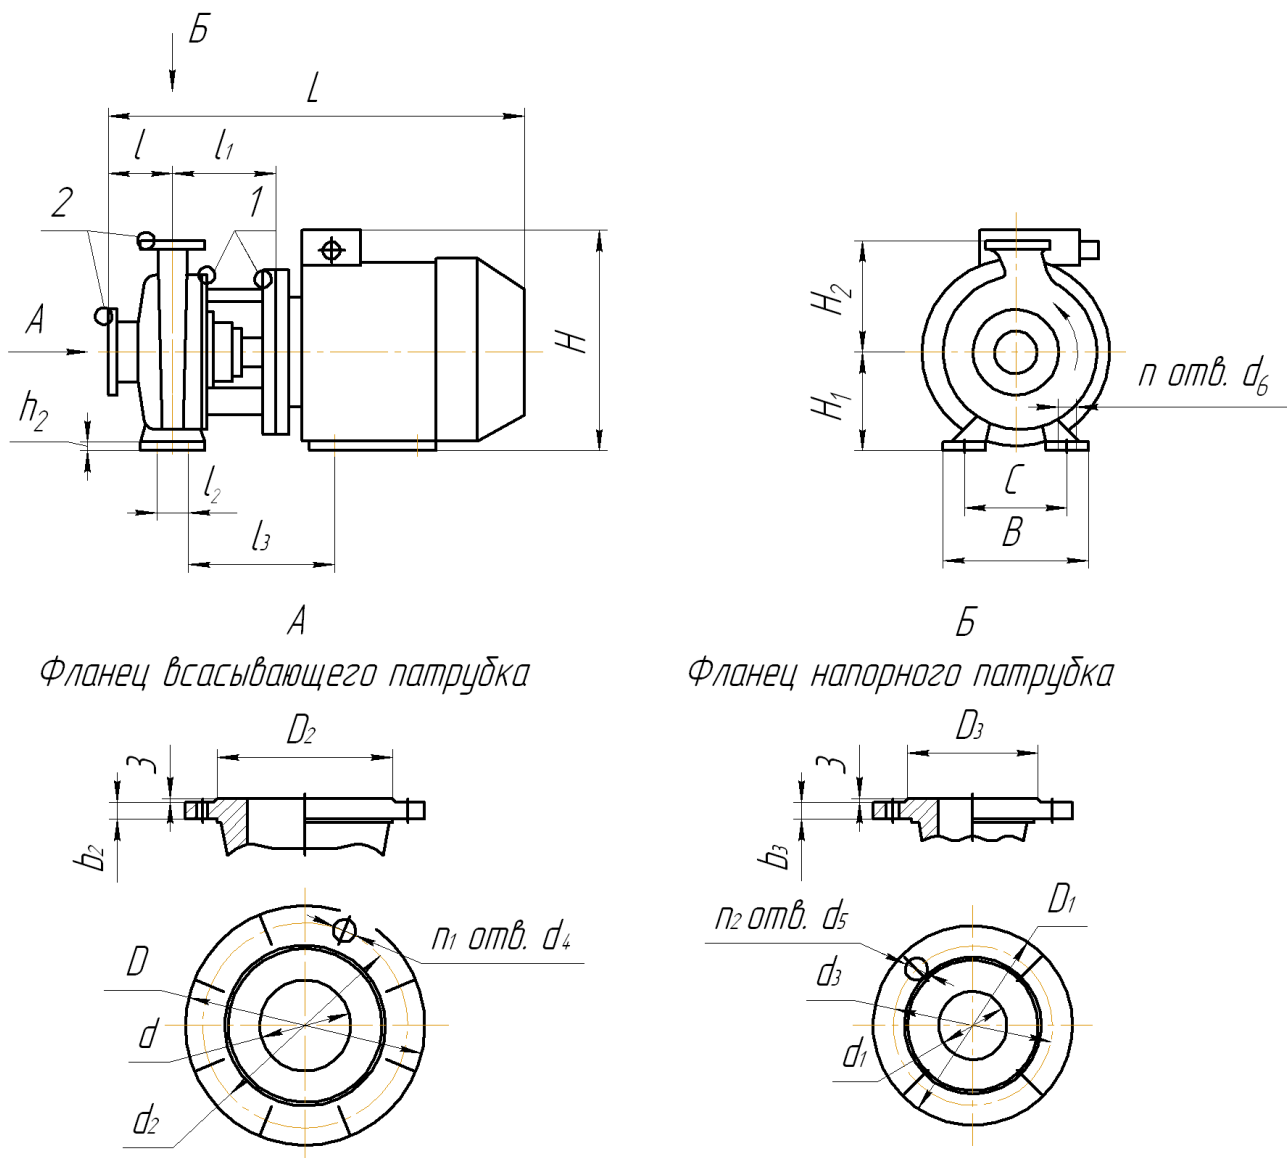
Габаритные и присоединительные размеры насосов типа «АХМ»
